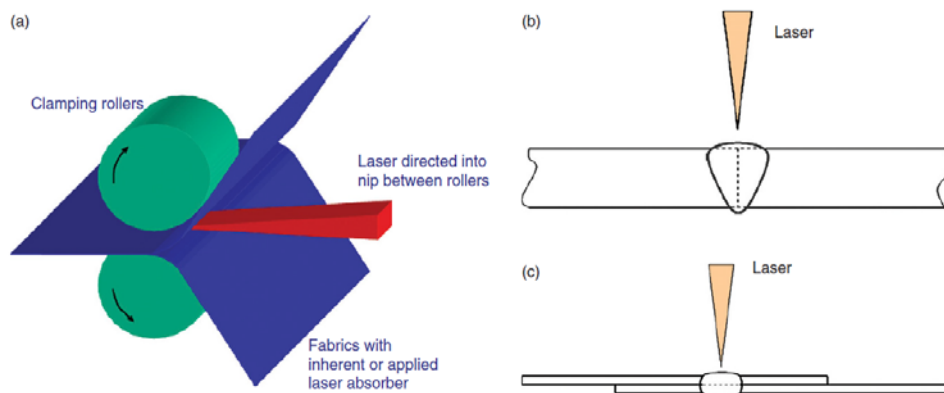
Soldadura láser directa: a) estrechamiento entre rodillos, b) soldadura a tope y c) capas de film superpuestas (Fuente: TWI Ltd).
